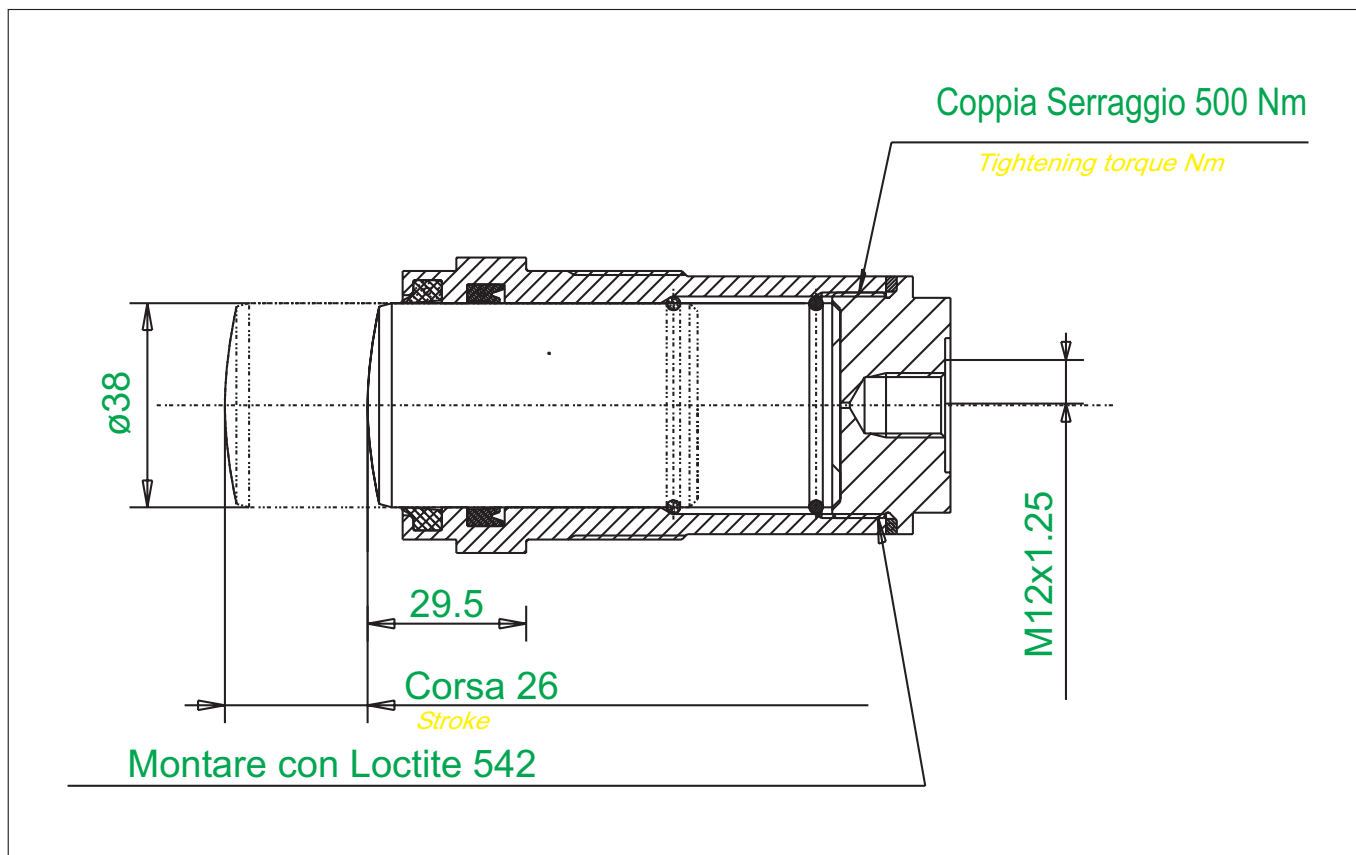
Vue du piston pour la régulation hydraulique du stabilisateur.
